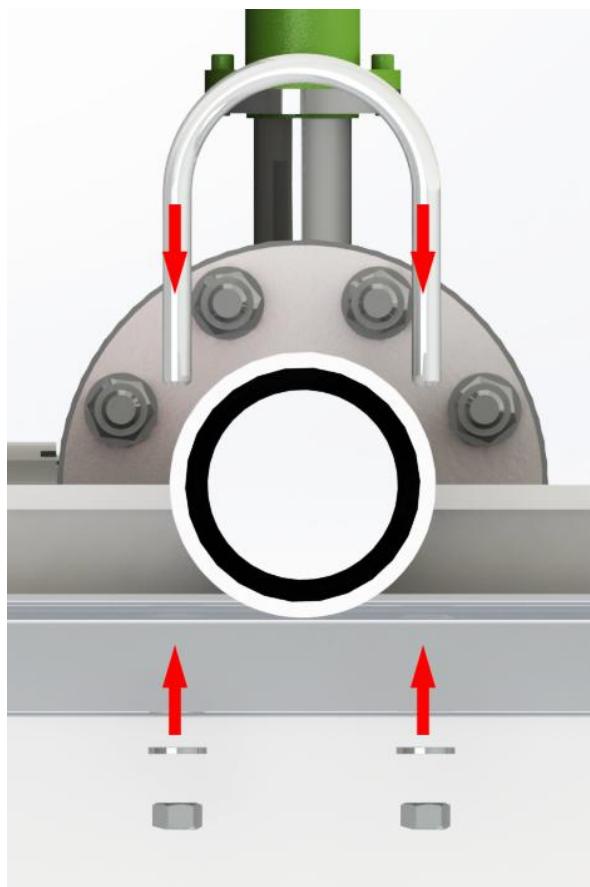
Установка хомута крепления к трубопроводу.
